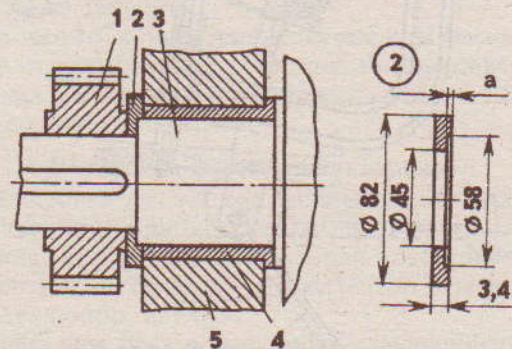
Узел передней опоры коленчатого вала: 1 - шестерня газораспределительного механизма; 2 - шайба; 3 - коленчатый вал; 4 - подшипник; 5 - опора подшипника. Размер "а" зависит от величины, на которую изношен буртик подшипника
